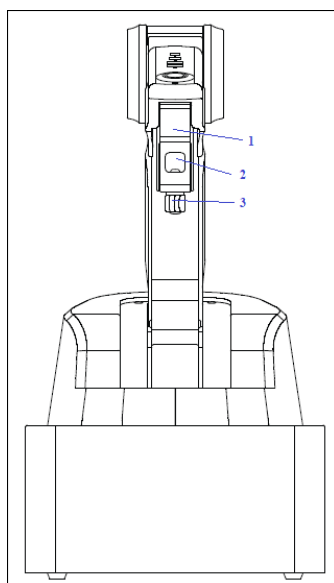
Манипулятор (вид спереди), где 1 – блок инструмента; 2 – гнездо фиксатора блока инструмента; 3 – прижимной винт
